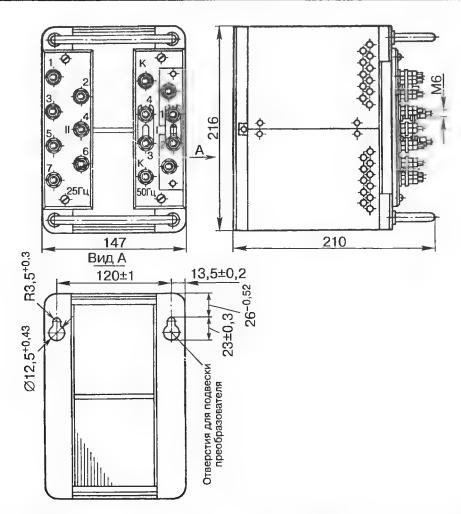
Ферромагнитный блок преобразователя ПЧ50/25-150
